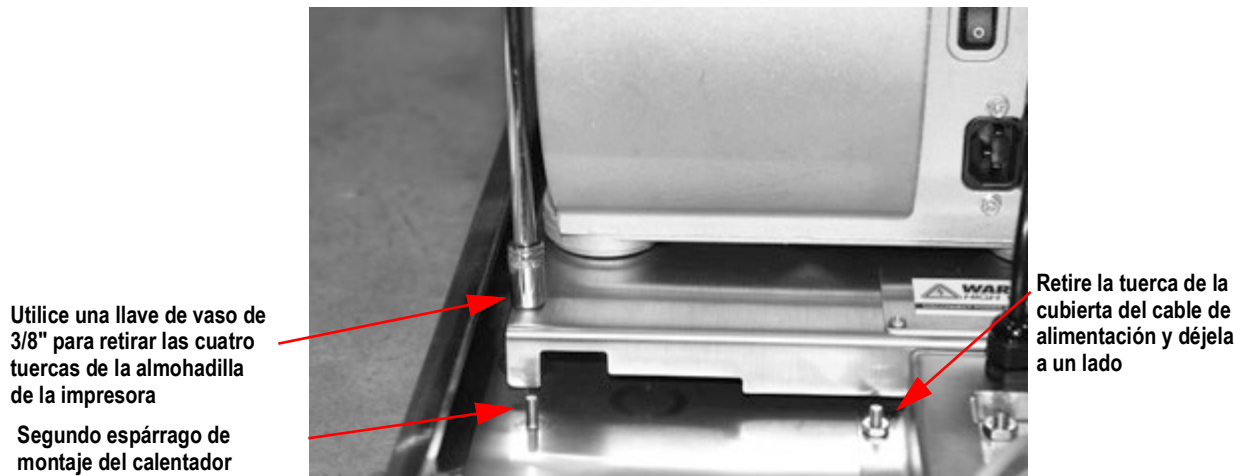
Desatornille las cuatro tuercas que sujetan la almohadilla de la impresora a la placa base de la impresora
